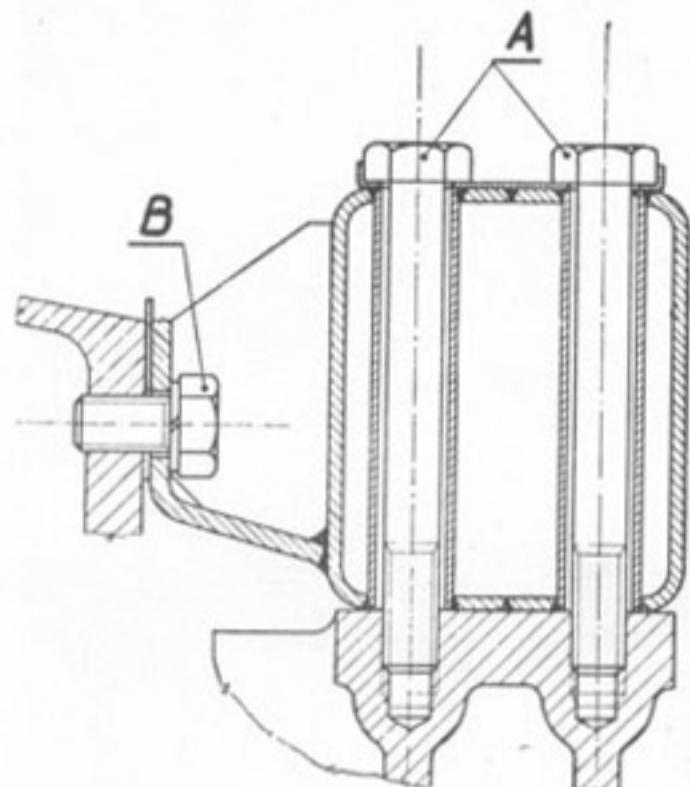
Přední pružné upevnění budky pro řidiče (na silentbloku).
